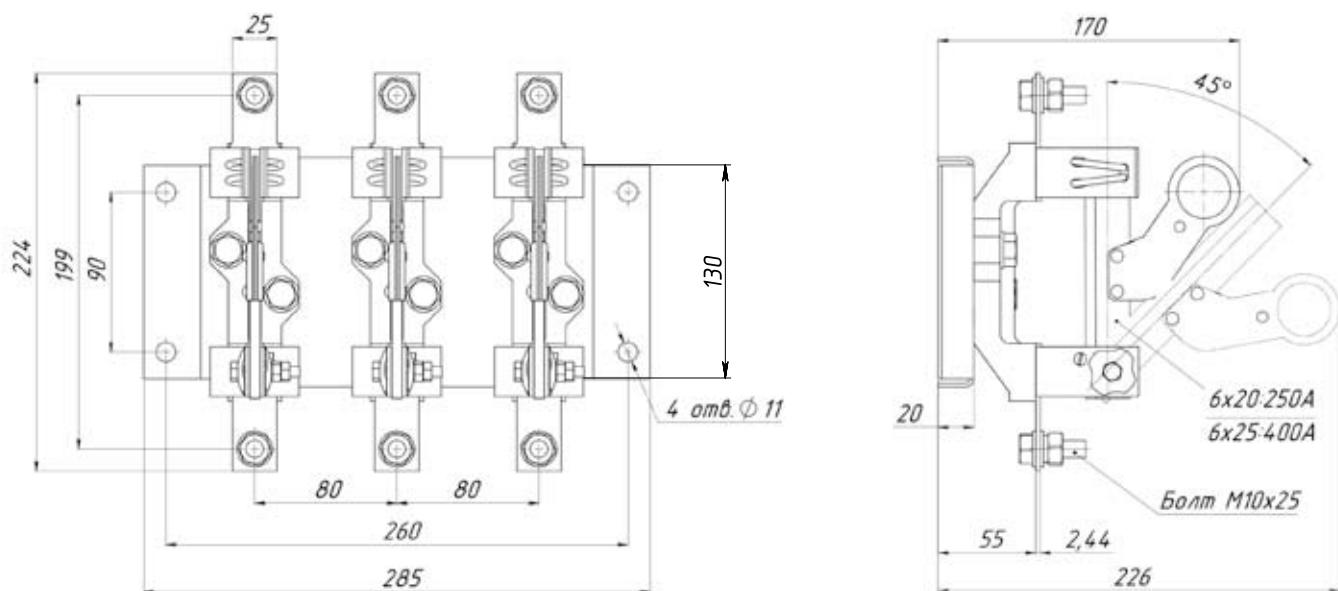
Разъединитель Р43 с пополюсным оперированием штангой ШО-1 на номинальный ток 250 А и 400 А
